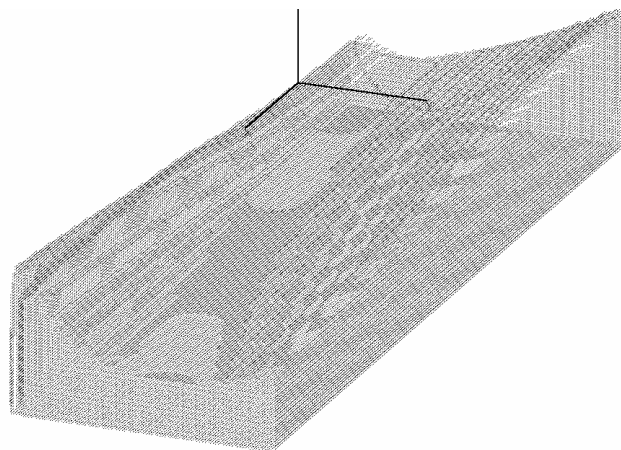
Заготовка детали (рис. 6), “обработанная” с одной стороны
